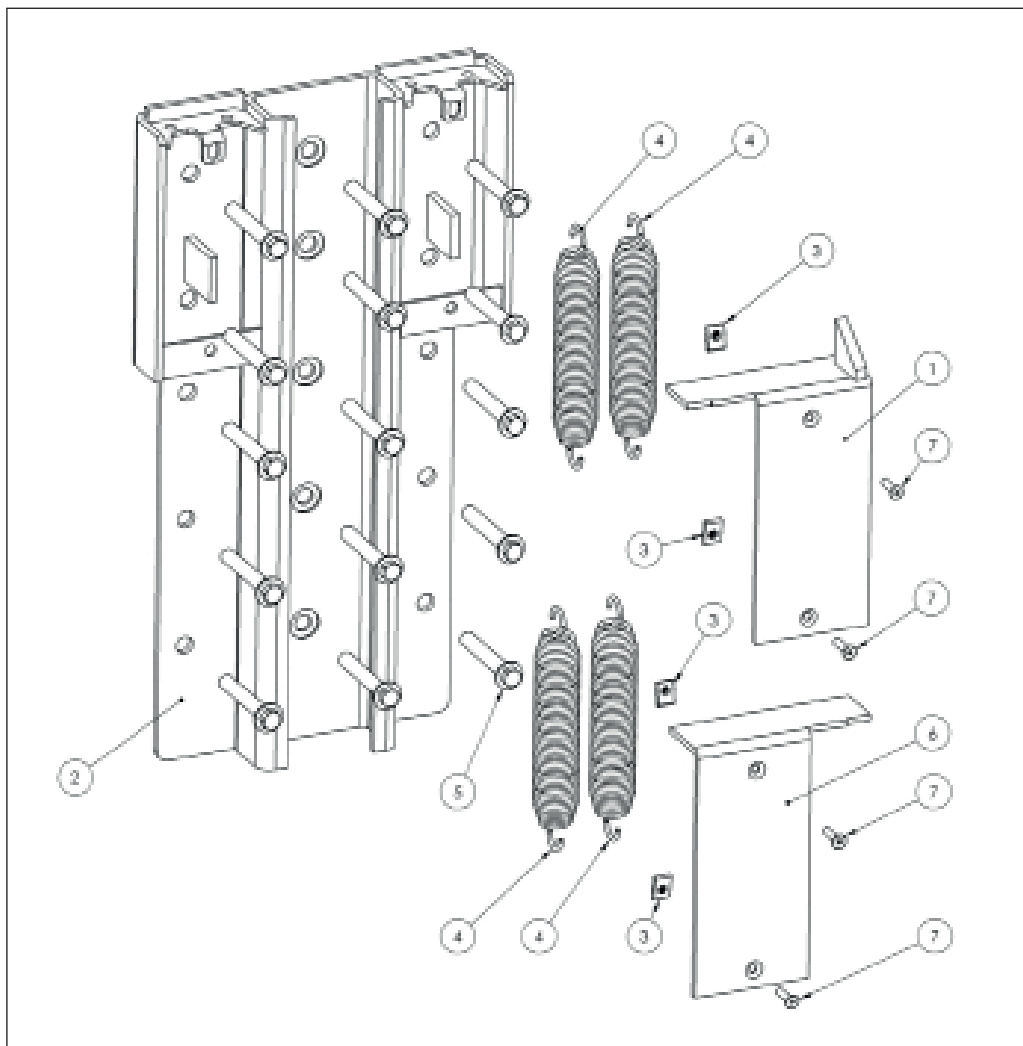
FIGURA AR—CONJUNTO DE GUÍA DE RODILLOS
